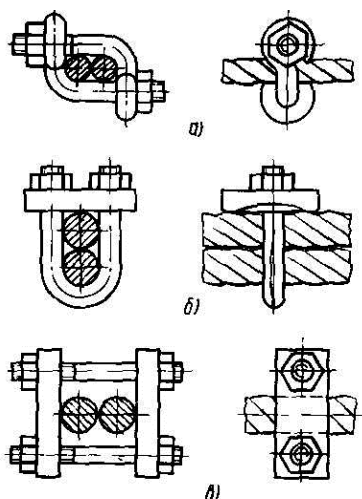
Затискувач для з'єднання тросів: а – з двома петлями; б - різковий; в - пластинчастий
